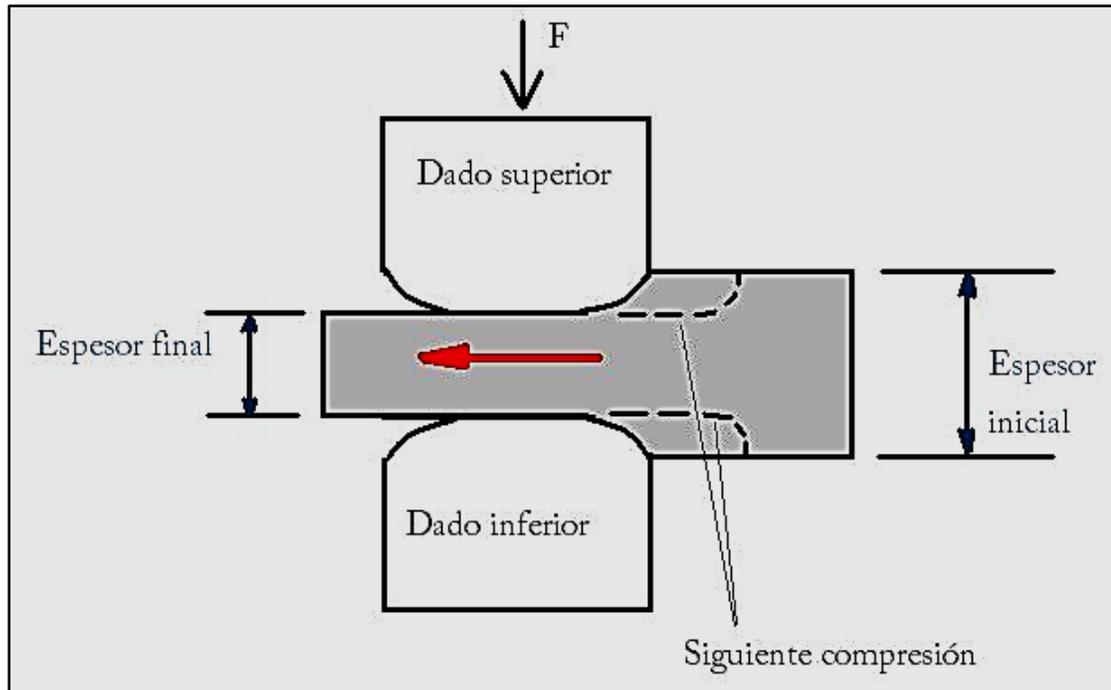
Fuerzas de compresión actuando sobre el metal
